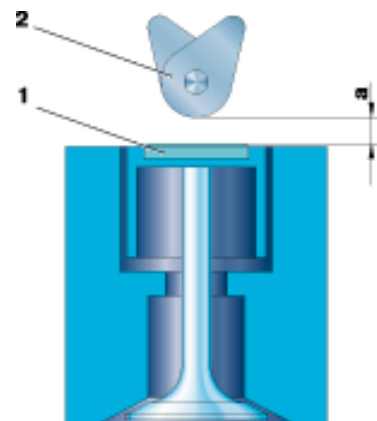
Схема измерения зазора в приводе клапанного механизма двигателя мод. F3R 272: 1 – регулировочная шайба; 2 – кулачок распределительного вала; а – зазор
